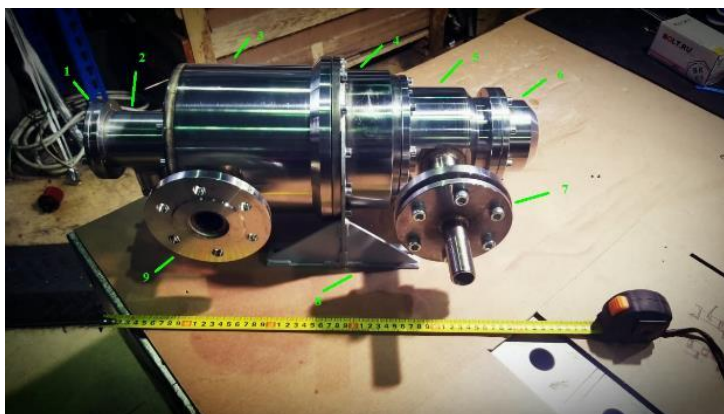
Прототип детандера: 1 - крышка электрической распределительной коробки; 2 - электрическая распределительная коробка; 3 - корпус генератора; 4 - промежуточный корпус (корпус муфты привода); 5 - кожух; 6 - крышка полости шестерен синхронизатора вращения роторов; 7 - входное отверстие труба; 8 - монтажный кронштейн; 9 - выпускная труба.
